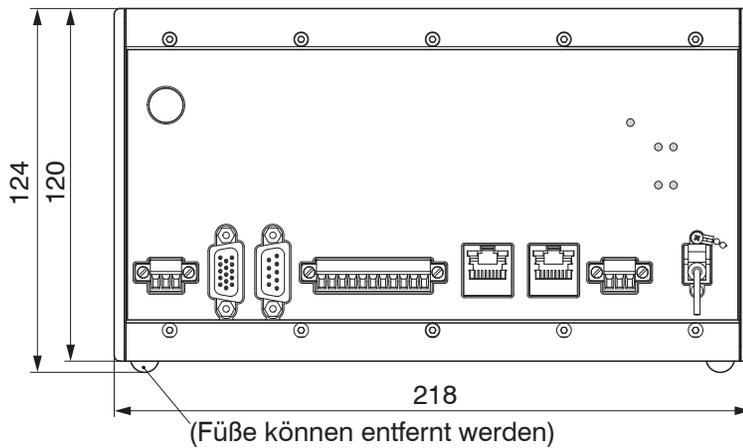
Maßzeichnung Frontansicht des Controllers IMC5x00, Abmessungen in mm
